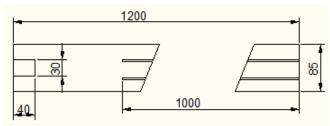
Soporte Principal. Vista Frontal [Diseño de autores]
